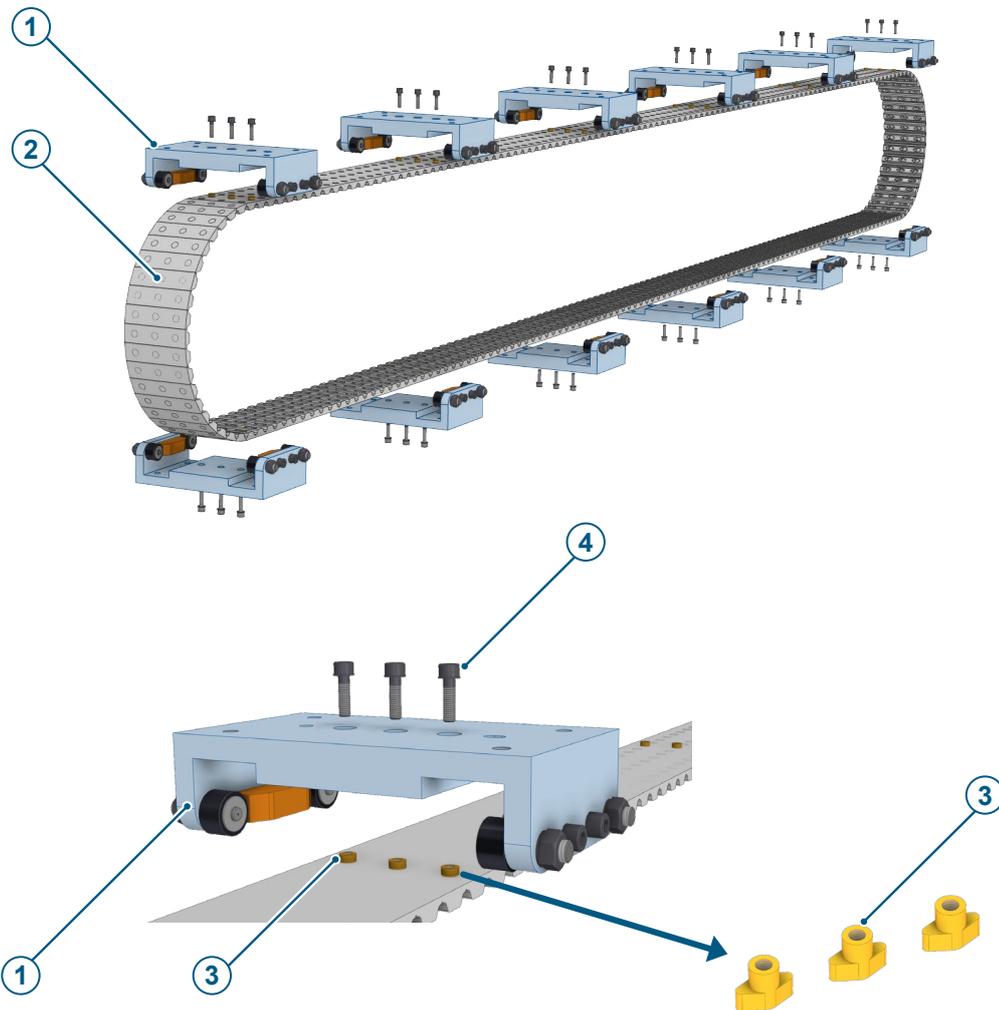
Montage der Werkstückträger auf dem Zahnriemen
